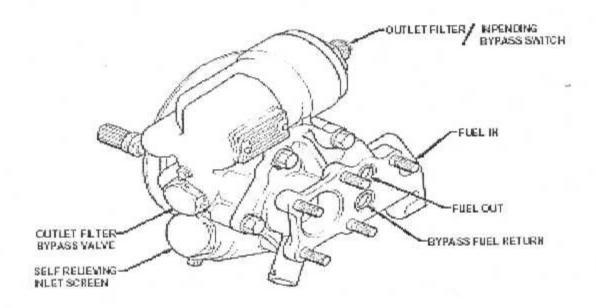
ASSEMBLAGE FILTRE / RECHAUFFEUR DU CARBURANT
